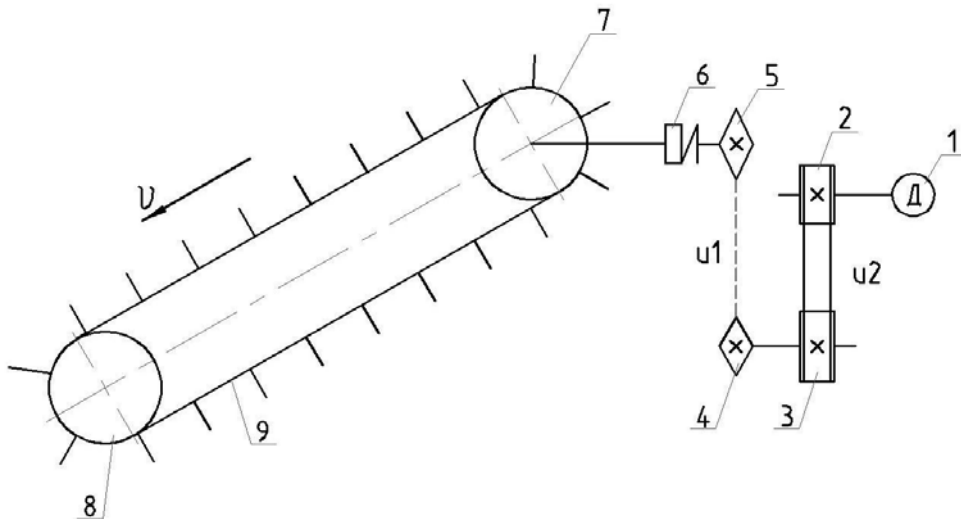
Кінематична схема скребкового конвеєра: 1 – двигун; 2, 3 – шкві пасової передачі; 4, 5 – зірочки ланцюгової передачі; 6 – муфта; 7 – приводна зірочка; 8 – натяжна зірочка скребкового конвеєра; 9 – ланцюг зі шкребками; u_1 і u_2 – передавальні числа ланцюгової і пасової передач відповідно
